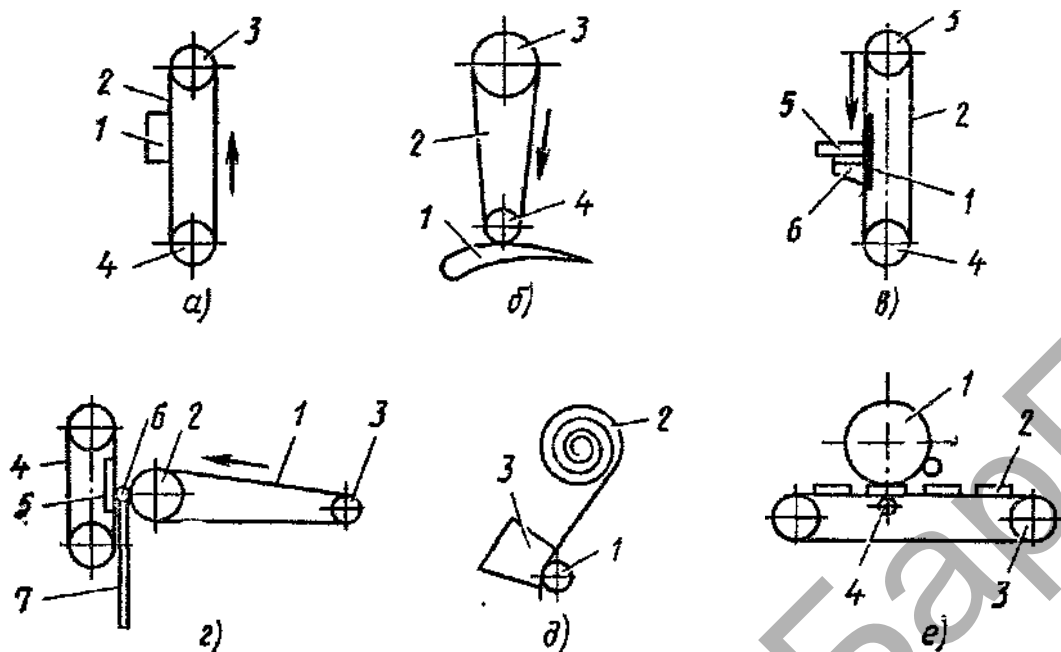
Основные схемы обработки шлифовальной лентой
